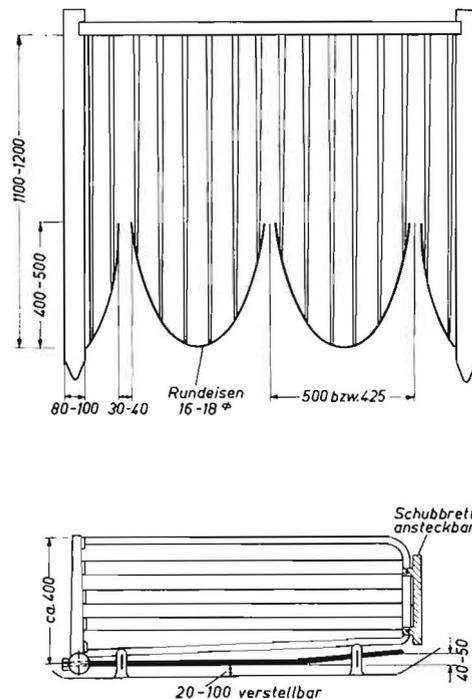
Zweckmäßige Ausbildung einer Futterrüben-Rodegabel
